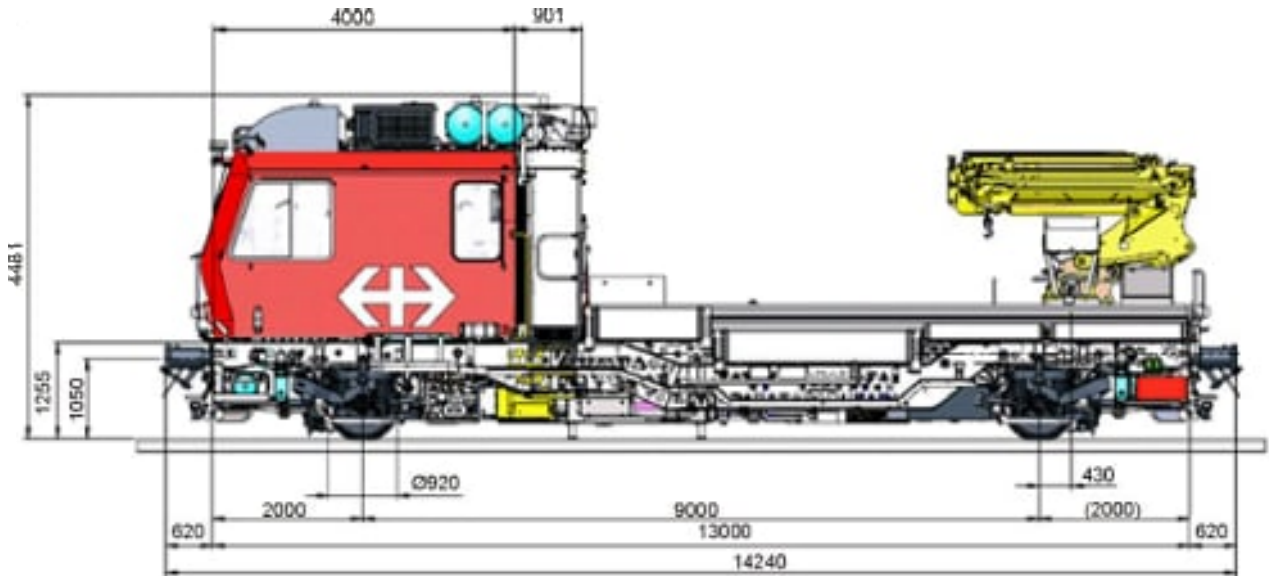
Fahrzeugabmessungen, Seitenansicht
